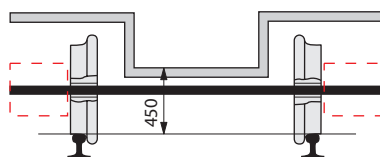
Колесная пара с наружным расположением тягового привода и тормозного оборудования
